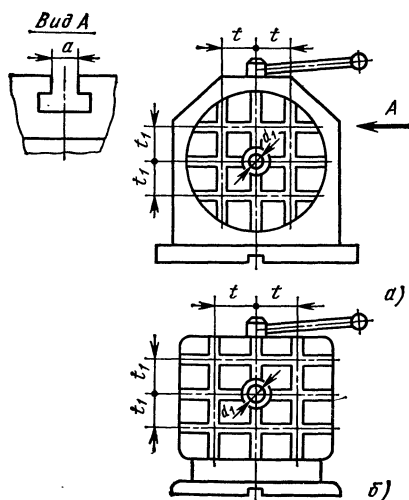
Унифицированные конструктивные элементы УБП для установки заготовок:
